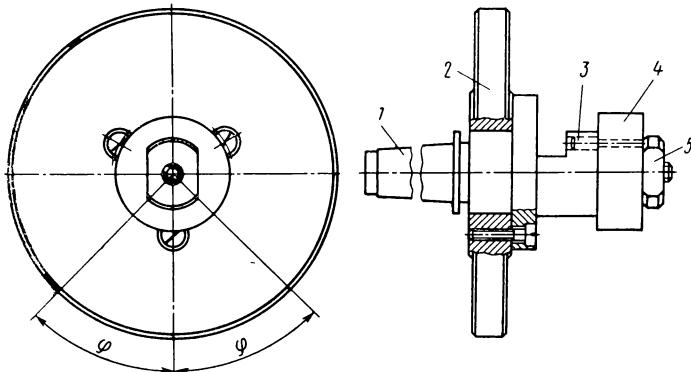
Элементы наладки приспособления для шлифования контура детали:
